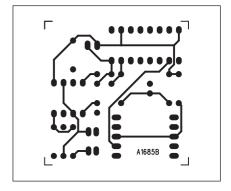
Obrazec desky spojů kostky (strana TOP)
